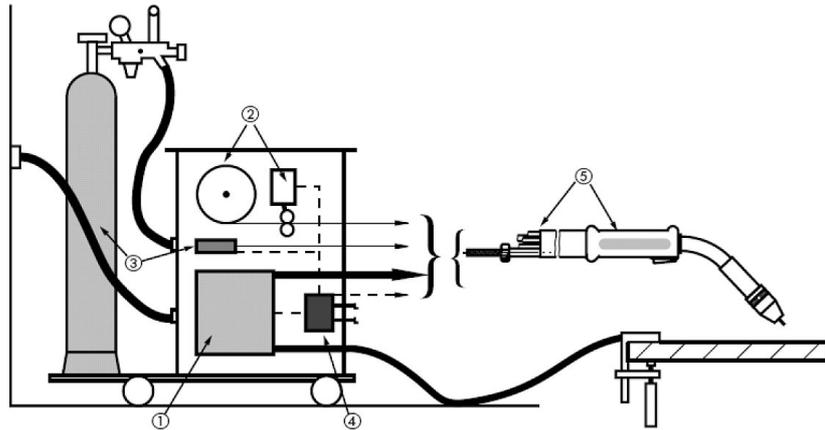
Funktionsprinzip Metall-Schutzgasschweißanlage
